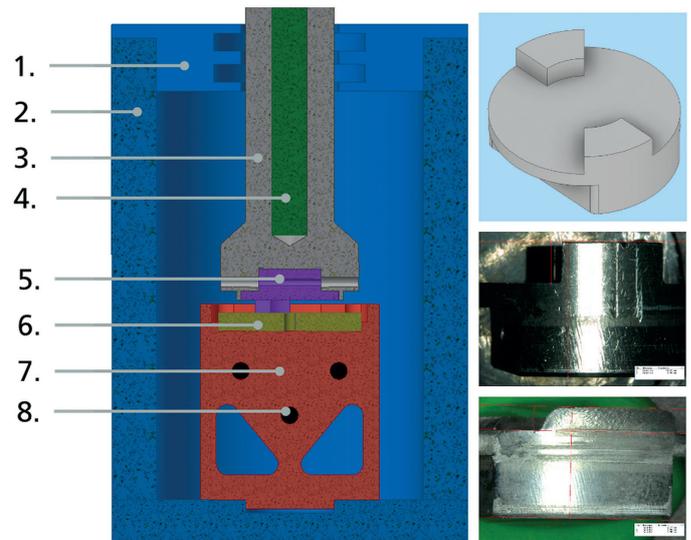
links - Versuchsaufbau: 1) Deckel, 2) Isolationsbehälter, 3) Probenhalter für die Al-Probe, 4) Heizelement, 5) Aluminiumprobe, 6) Plattenprobe, 7) Plattenprobenhalter, 8) Heizelemente; rechts – Geometrie der Aluminiumprobe (oben), Foto der Aluminiumprobe vor (Mitte) und nach der Umformung (unten)
